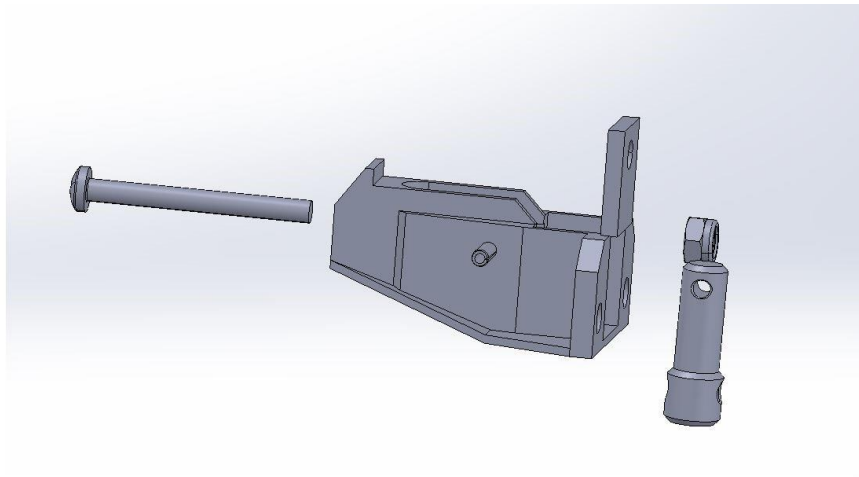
Vue éclatée d'un sous-ensemble mécanique modélisé sous SolidWorks.
